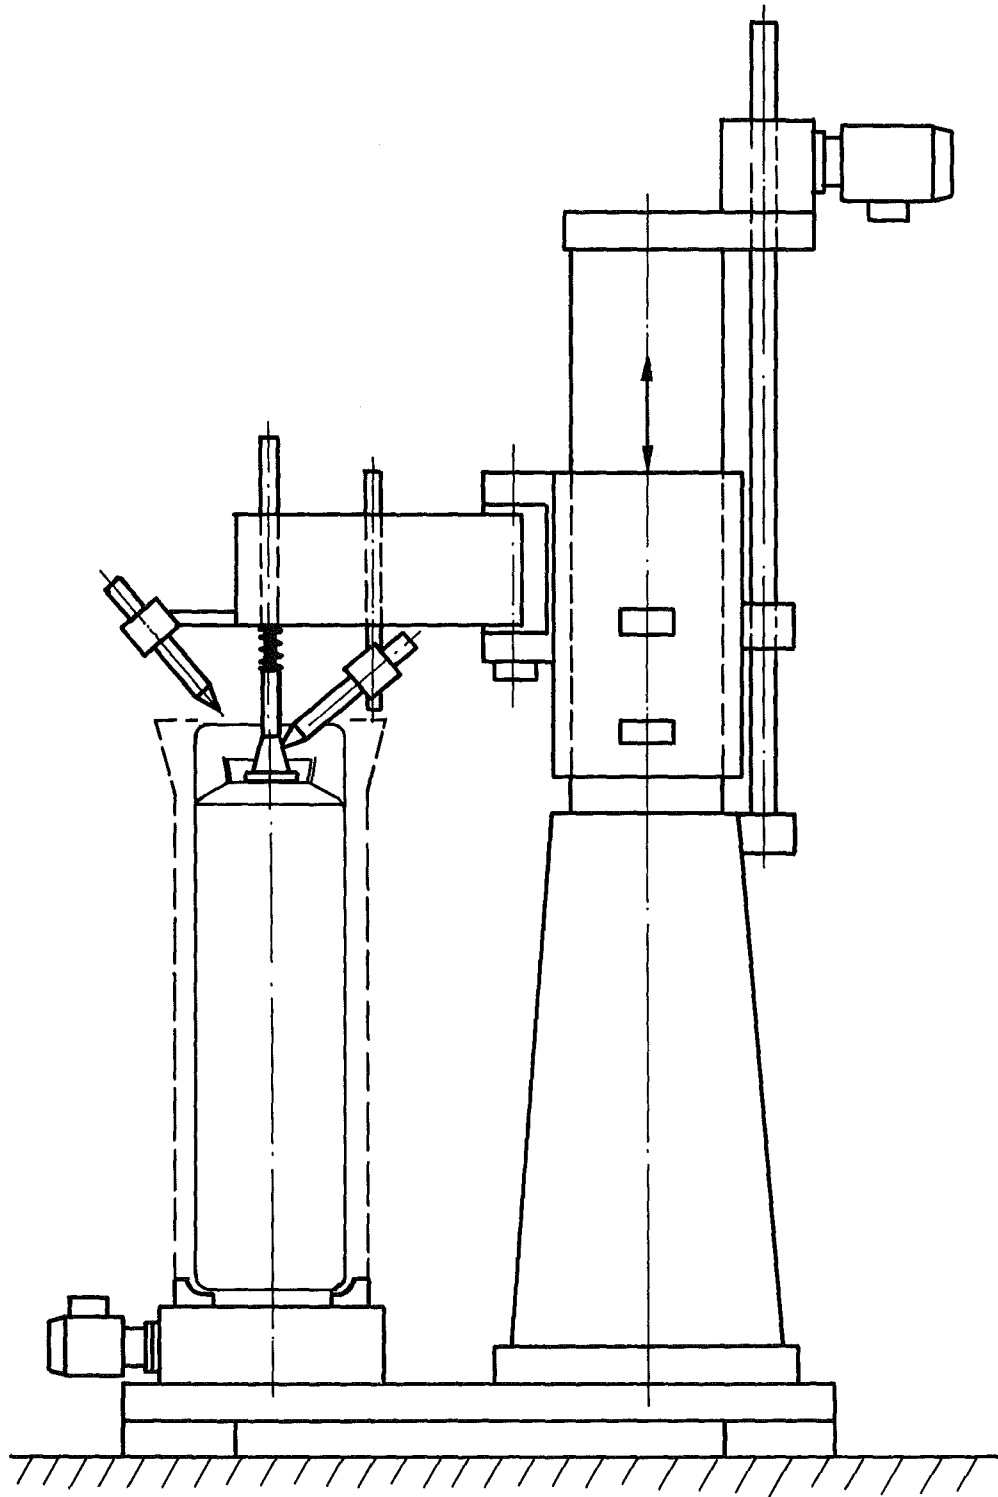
Prinzipieller Schweißstandaufbau
